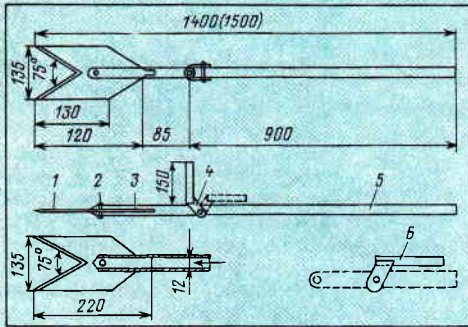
Устройство: 1 — режущий нож, заточка двусторонняя; 2 — заклепка, соединяющая нож с рукояткой; 3 — прорез в трубе; 4 — педаль откидная (для удобства при транспортировке) из узкой трубы; 5 — рукоятка (из водопроводной трубы); 6 — педаль — трубка (к ней приварены косынки).
